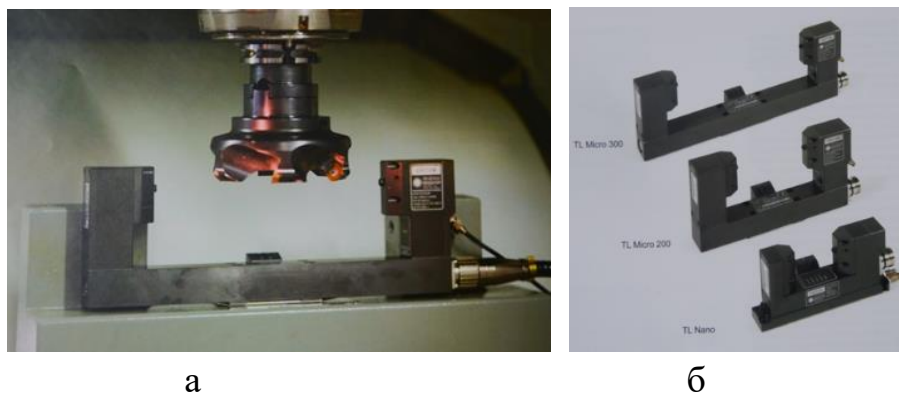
Лазерні системи вимірювання інструментів TL: а – на верстаті під час вимірювання; б – конструкції для різних розмірів інструменту
